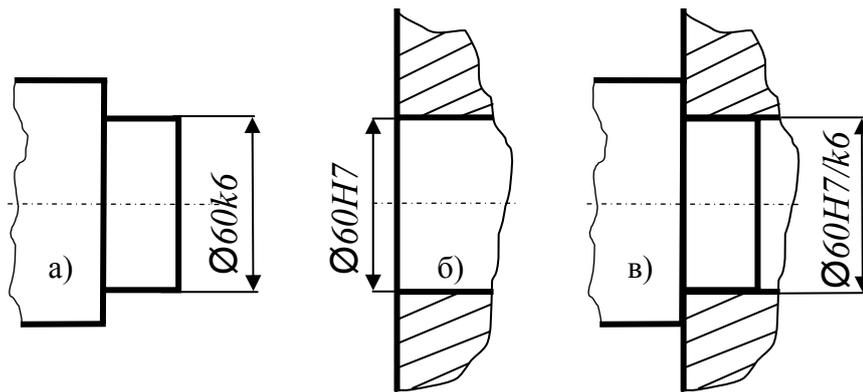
Допуск вала, допуск отверстия и сопряжение вала с отверстием. Посадка переходная. Система отверстия.
